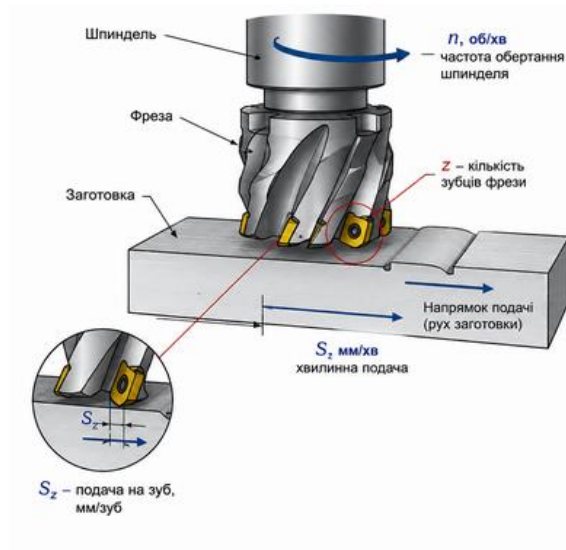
Схема визначення подачі при фрезеруванні[12]
